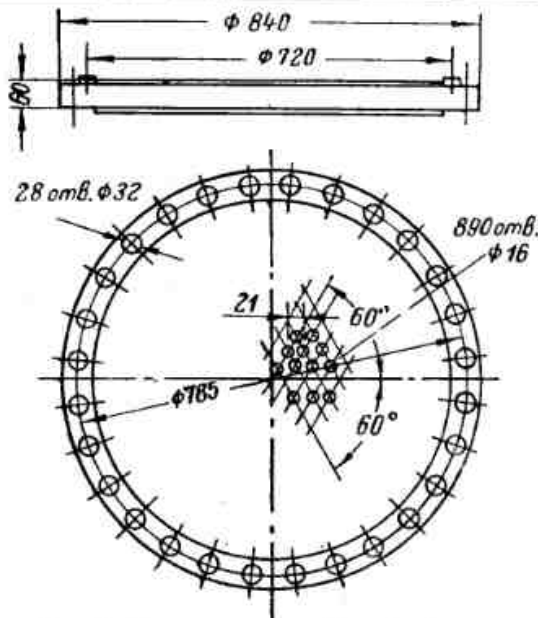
К расчету круглой трубной доски, не подкрепленной связями.
